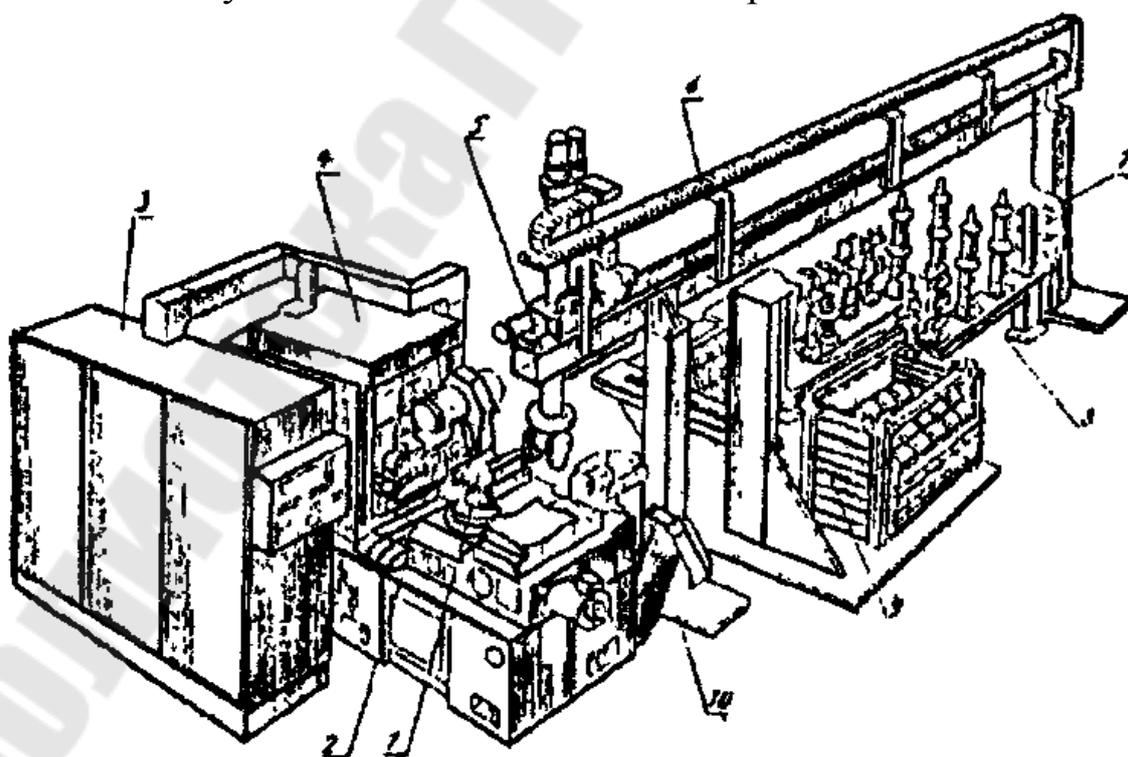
РТК на базе зубофрезерного станка для обработки зубчатых колёс
